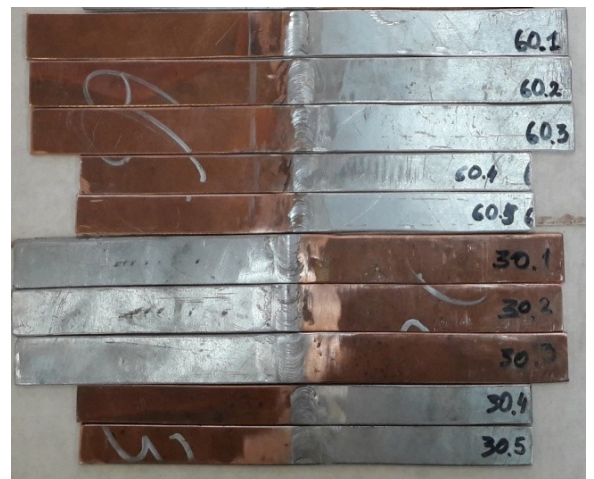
Внешний вид разнородных сварных соединений:
